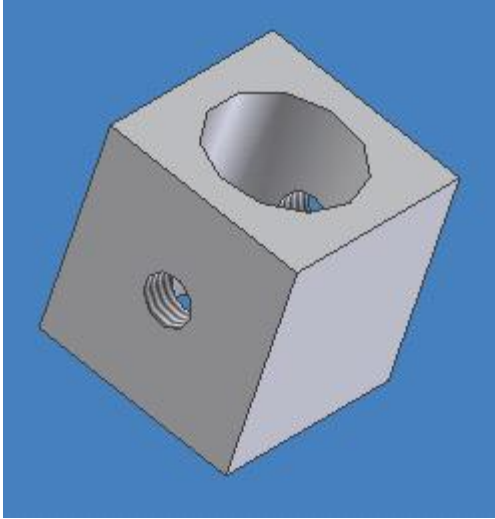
Pieza A5 . Se observa el mecanizado aplicado a 24 piezas según el plano AND00 - 0700
